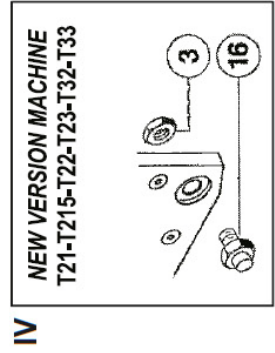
12 PERNI FISSAGGIO TESTATE / HEAD-ATTACHMENT PINS / BEVESTIGINGSPINNEN KOPPEN
